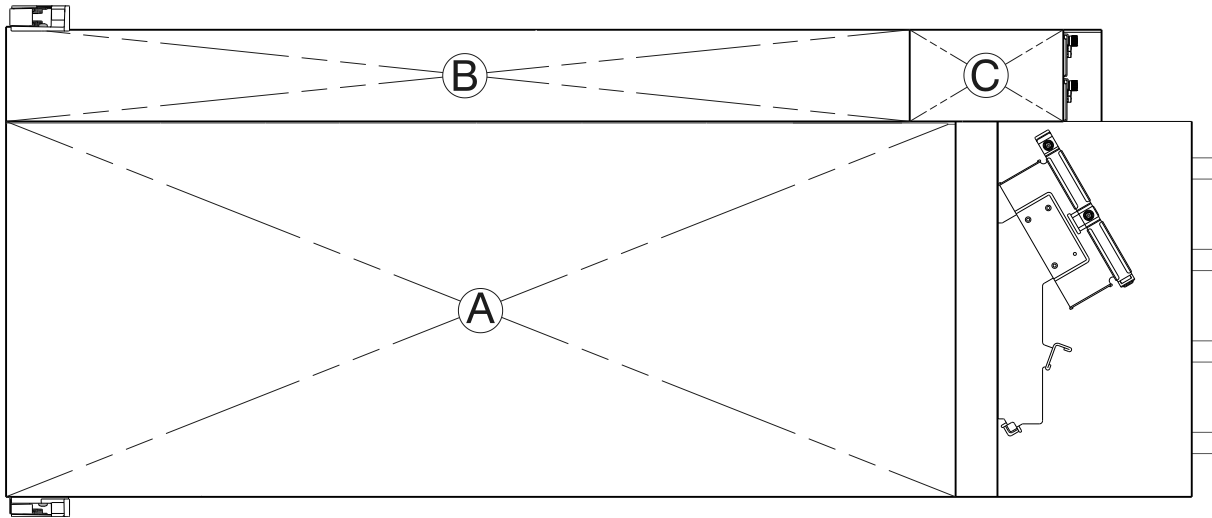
Alojamiento de expansión Modelo 106 – panel superior con cubiertas instaladas
